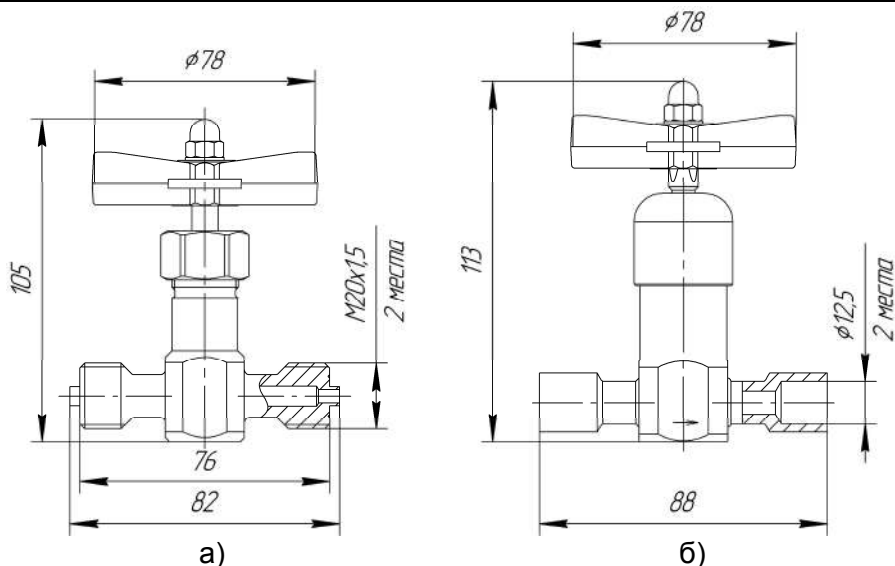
Габаритно- присоединительные размеры изделий ВИГ160-С1Б1Б (а) и ВИГ250-Н12С12С(б)
